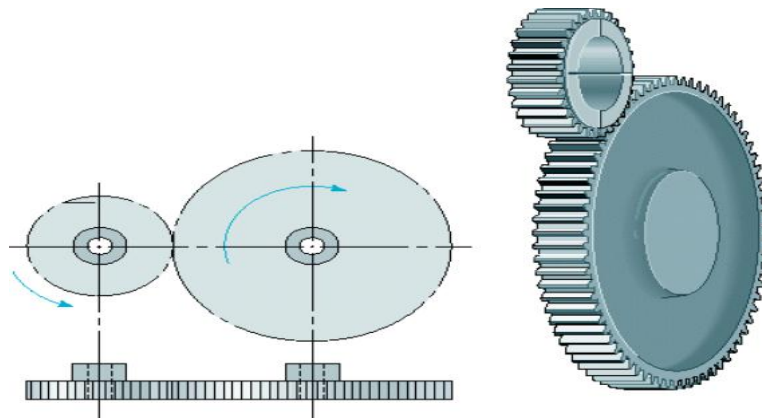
Engranaje cilíndrico de dientes rectos.
